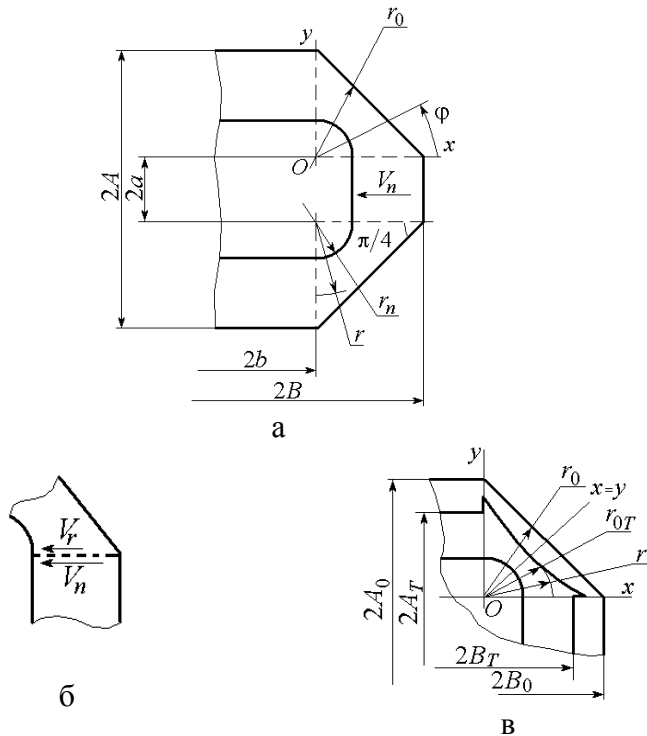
Вытяжка прямоугольной коробки с малыми угловыми радиусами: а - заготовка и поле скоростей; б - план скоростей на линии разрыва; в - схема перемещения фланца
